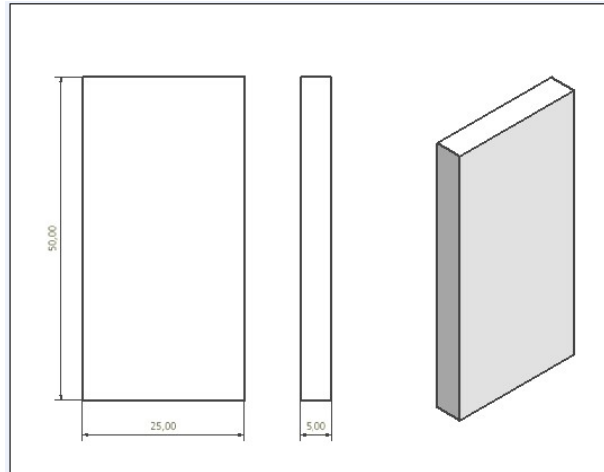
29. Dimensiones de la probeta para el ensayo ASTM G48
